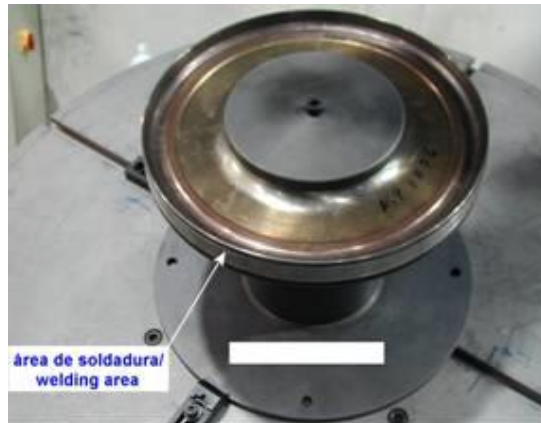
Utillaje para montar el cierre de cuchillas en la mesa de la máquina de soldadura orbital.
